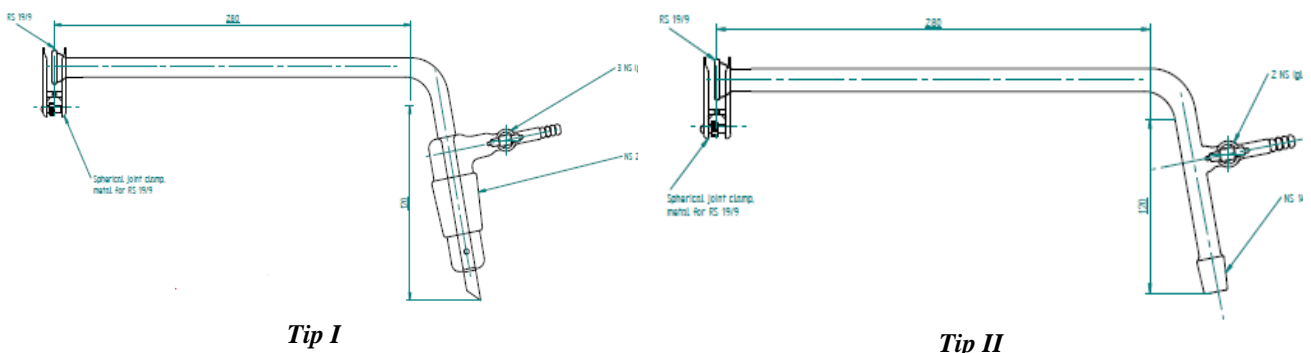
Adaptor pentru conectare balon cu gat rodat la linia de vid - Componenta si dimensiuni
